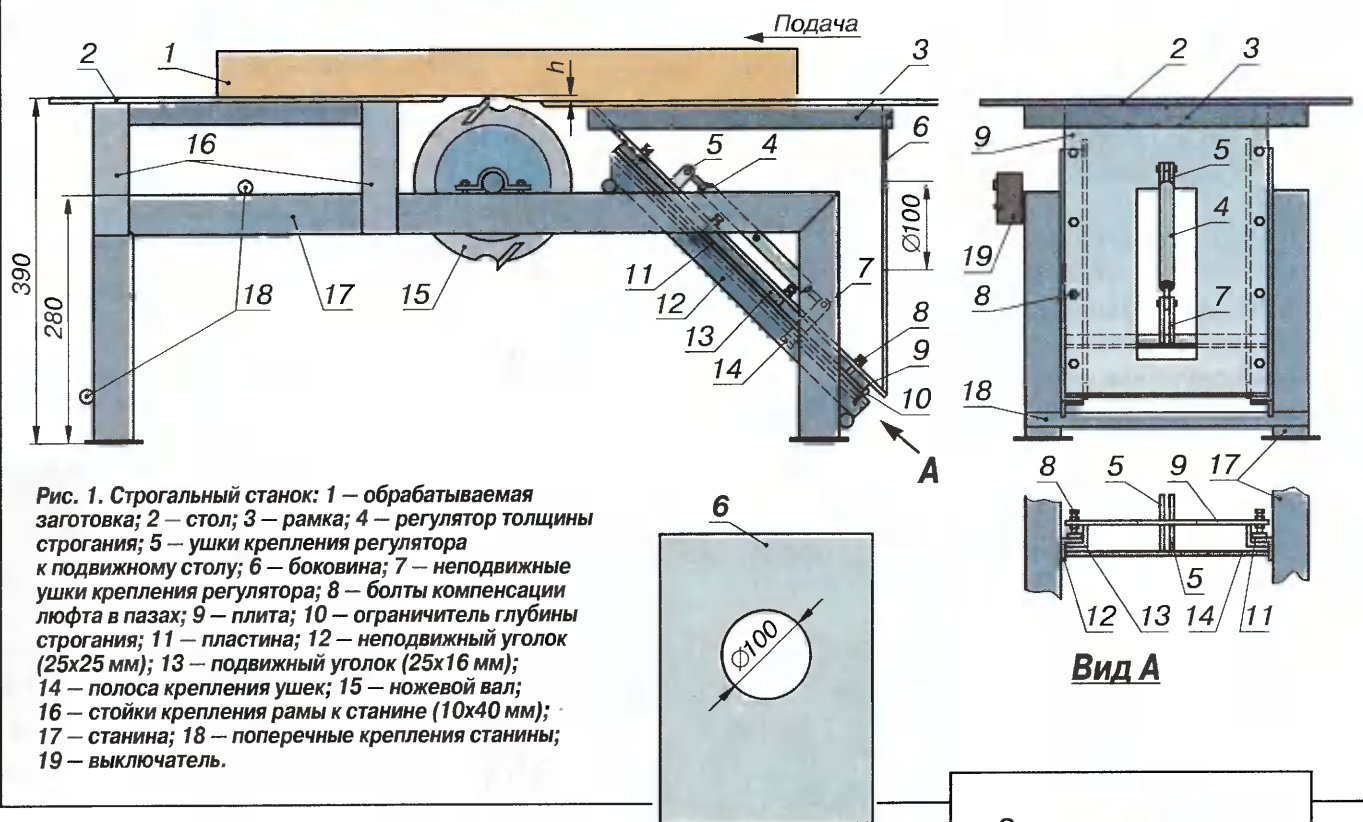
Строгальный станок: 1 — обрабатываемая заготовка; 2 — стол; 3 — рамка; 4 — регулятор толщины строгания; 5 — ушки крепления регулятора к подвижному столу; 6 — боковина; 7 — неподвижные ушки крепления регулятора; 8 — болты компенсации люфта в пазах; 9 — плита; 10 — ограничитель глубины строгания; 11 — пластина; 12 — неподвижный уголок (25x25 мм); 13 — подвижный уголок (25x16 мм); 14 — полоса крепления ушек; 15 — ножевой вал; 16 — стойки крепления рамы к станине (10x40 мм); 17 — станина; 18 — поперечные крепления станины; 19 — выключатель.
